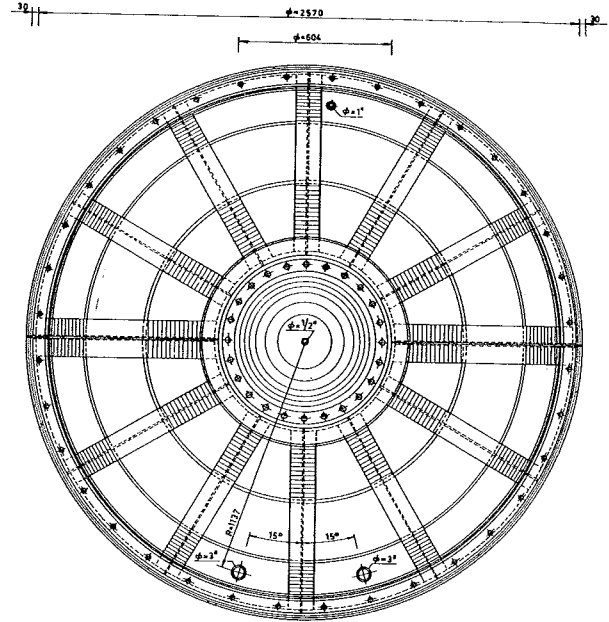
Dispositivo d'isolamento; parte centrale comune ai tre tipi: vista dall'esterno.
